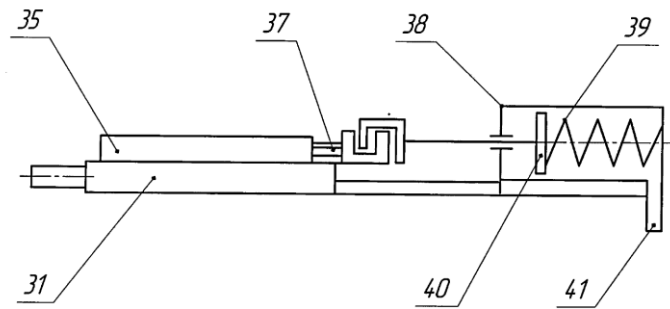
Схема з'єднання вкладиша з поршнем: 31 - підстава; 35 - повзун; 37 - вкладиш; 38 - пневмоциліндр; 39 - пружина; 40 - поршень; 41 - патрубок
